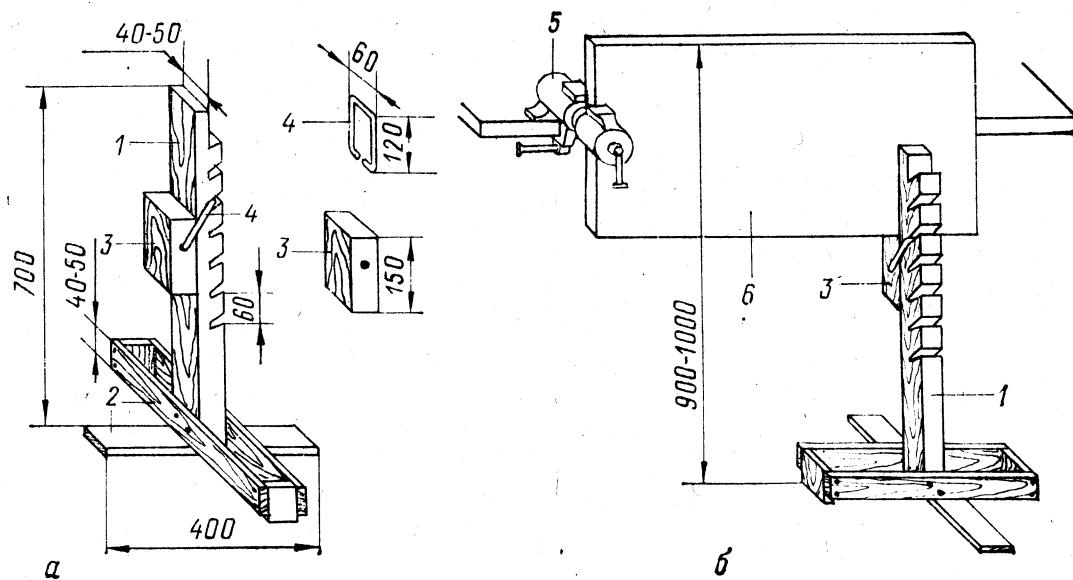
Подставка для опирания плиты при строгании и закрепление обрабатываемой плиты; 1 — стойка; 2 — крестовина; 3 — ползун; 4 — скоба; 5 — тиски; 6 — плита
